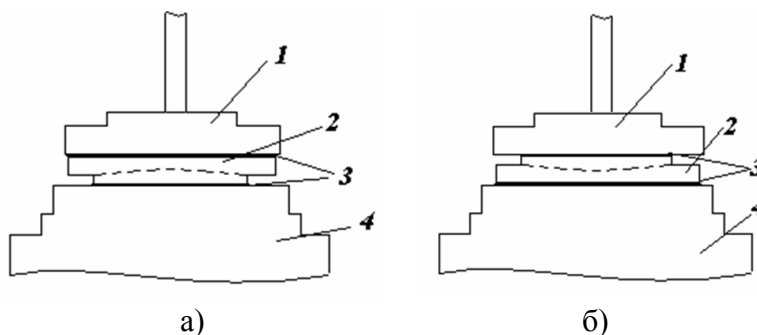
Конструкции диодов КД2969: а) спай катода с основанием корпуса; б) спай анода с основанием корпуса, где 1 – верхний вывод конструкции; 2 – полупроводниковая структура; 3 – припой; 4 – основание корпуса.
